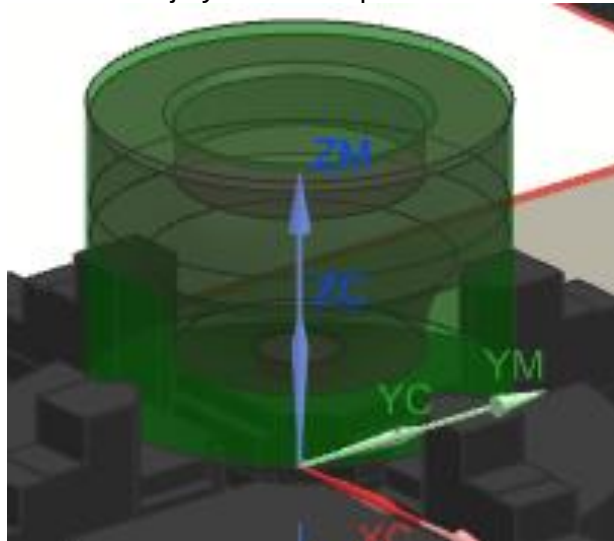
Tipo de montaje propuesto para la mecanización del impeller
